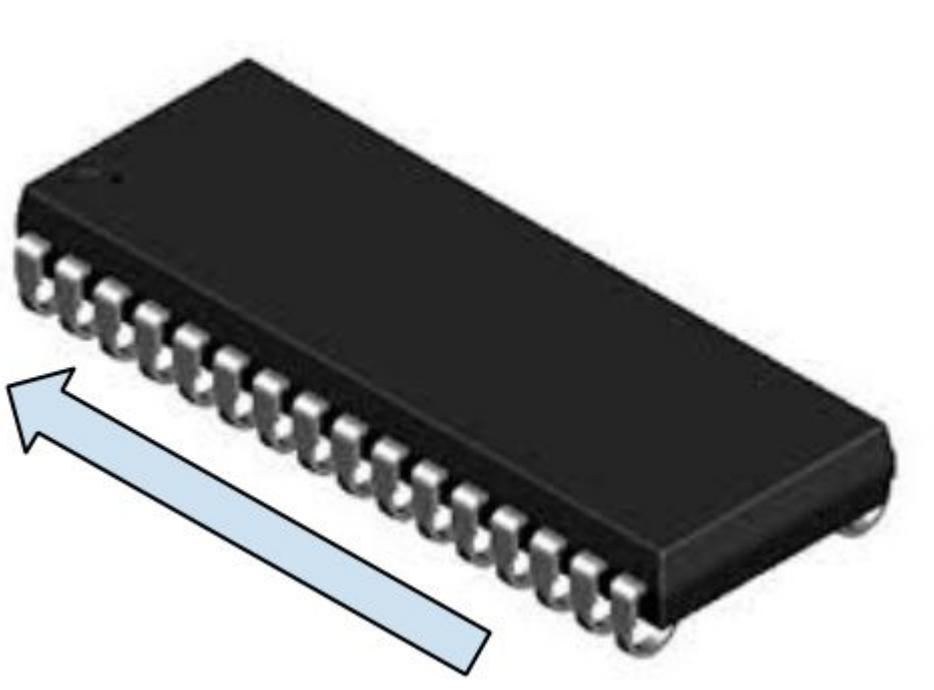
Dirección correcta para la soldadura por ola de circuitos integrados.
